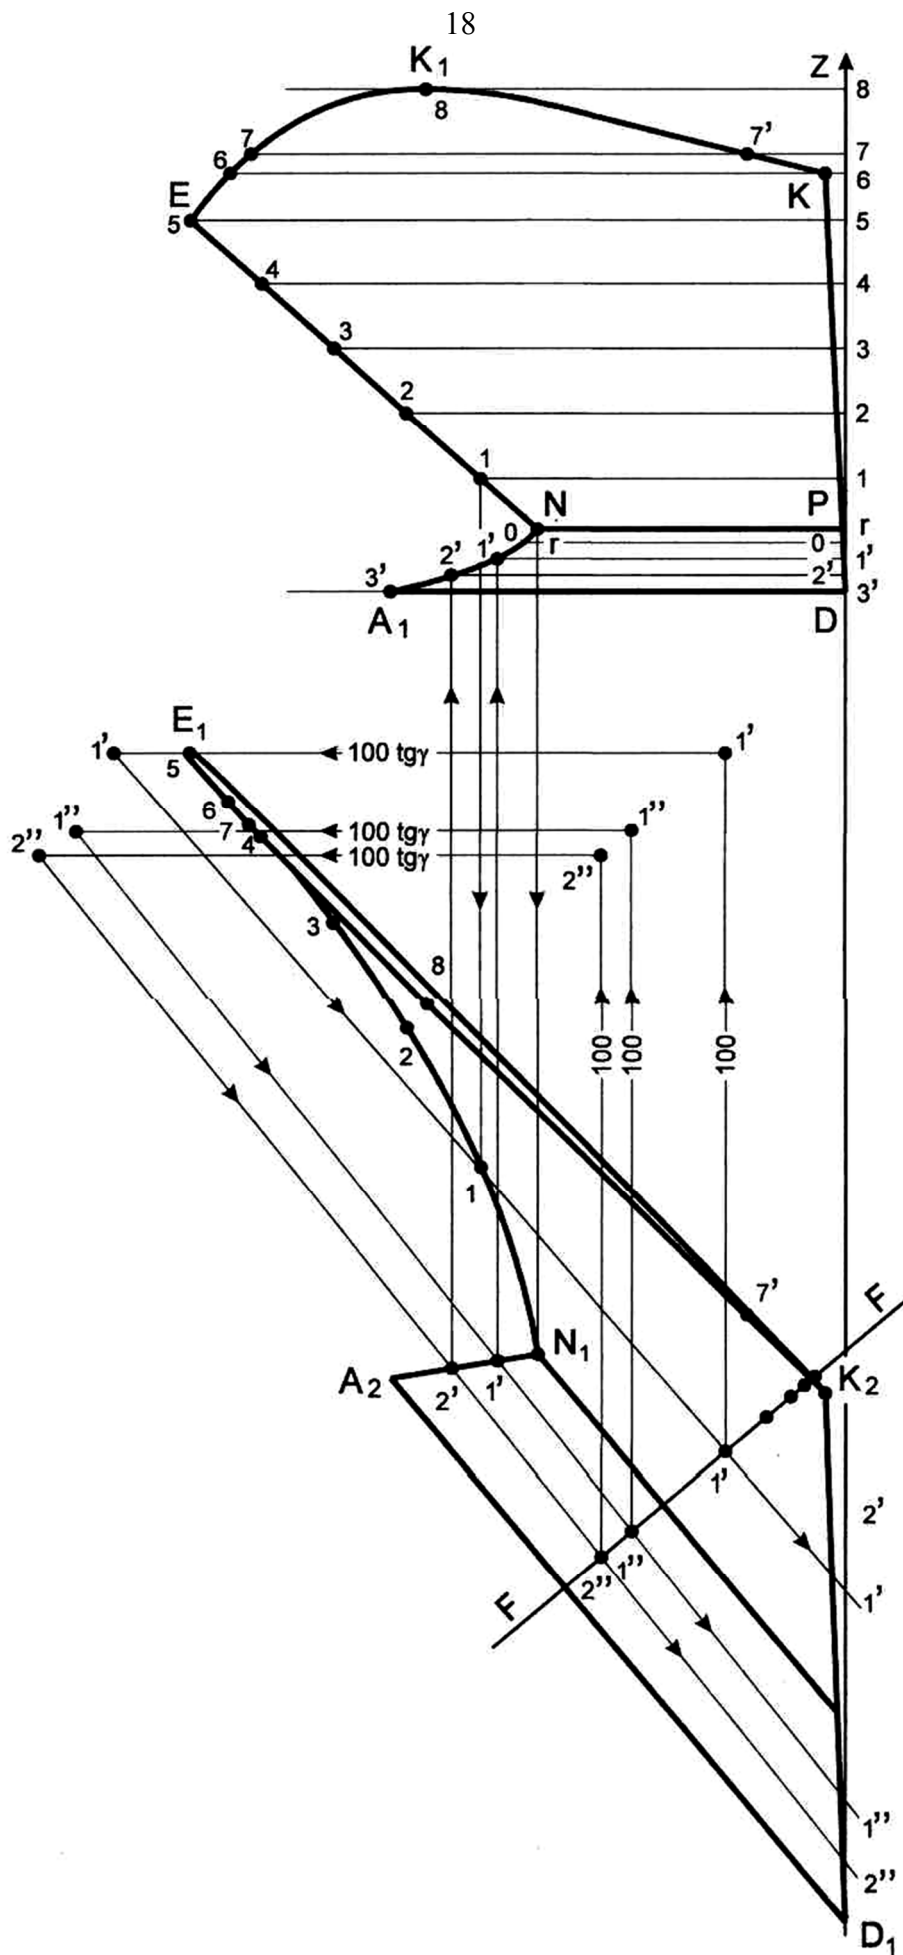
Побудова робочої поверхні плужного корпусу
